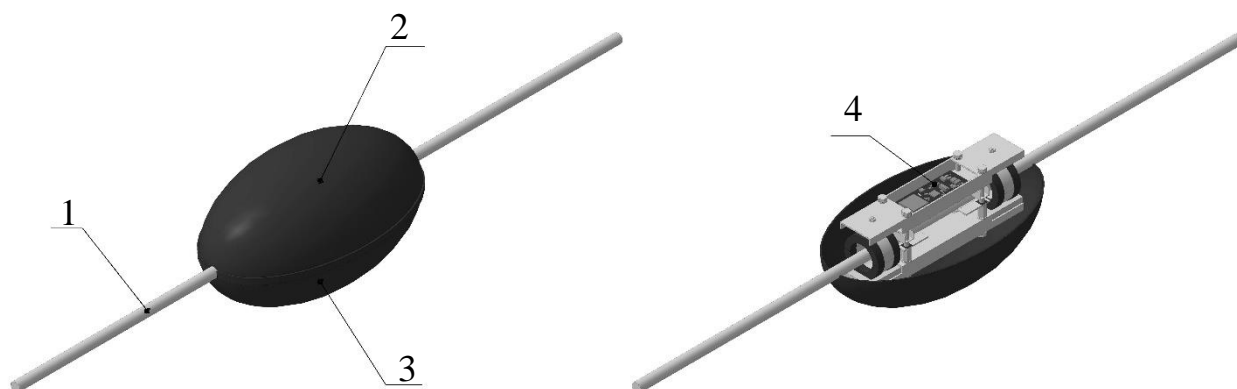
Конструкция датчика: 1 – повод линии электропередач, 2,3 – внешний пластиковый корпус, 4 – аппаратная часть платформы.
